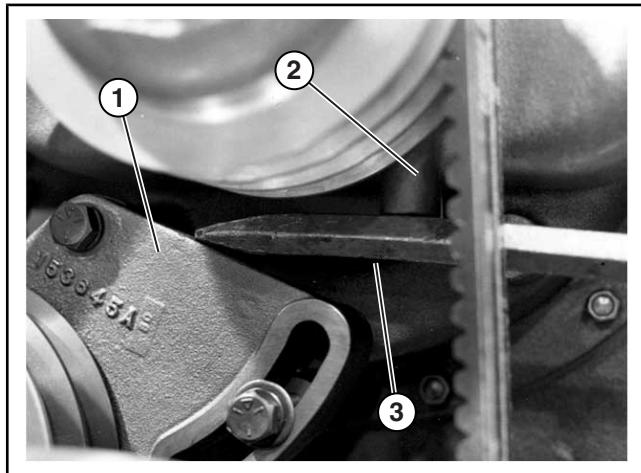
Натяжение приводного ремня водяного насоса контура рубашки
